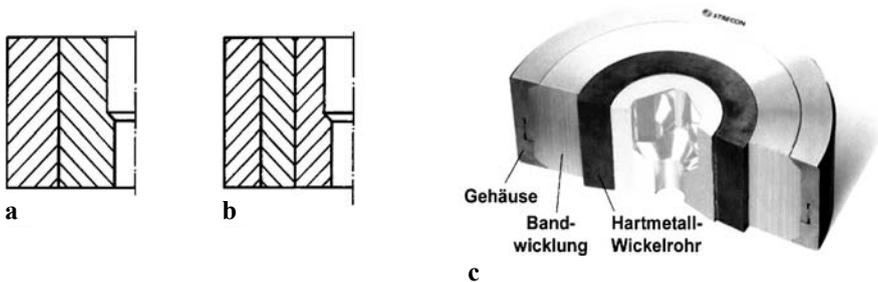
Armierung von Fließpressmatrizen: a mit einem Armierungsring [1.1], b mit zwei Armierungsringen, c durch Umwickeln mit hochfesten, vorgespannten Stahlbändern (Bandarmieren) [1.3]
